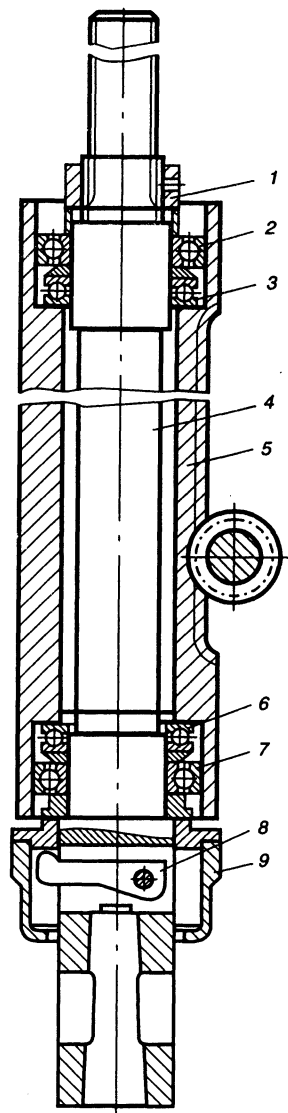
Шпиндельный узел вертикально-сверильного станка
